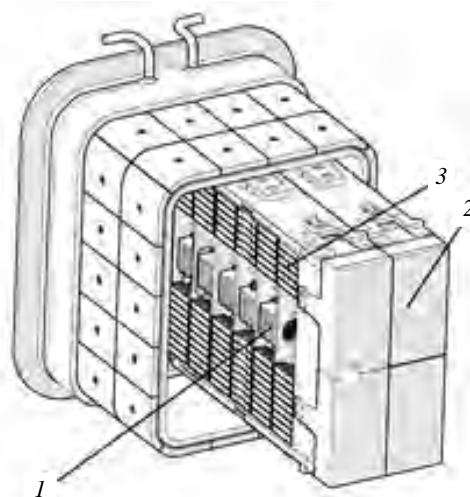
Внешний вид конструкции портовой заглушки № 11 (экваториальный порт EQ11), в которой расположен нейтронный коллиматор: 1 — коллиматор, состоящий из пяти блоков; 2 — диагностическая первая стенка; 3 — элементы нейтронной защиты портовой заглушки. На рисунке не показаны внутривортовые элементы других диагностик и скрыт один из трёх диагностических защитных модулей
